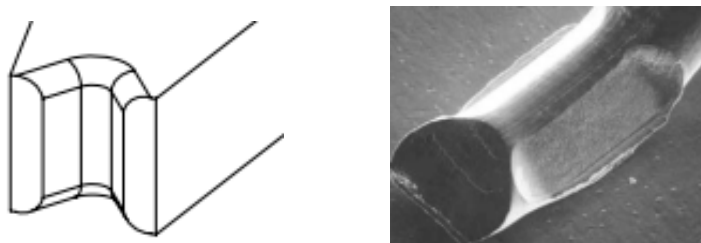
Detail hrotu klínového nástroje se dvěma paralelními drážkami [28].
